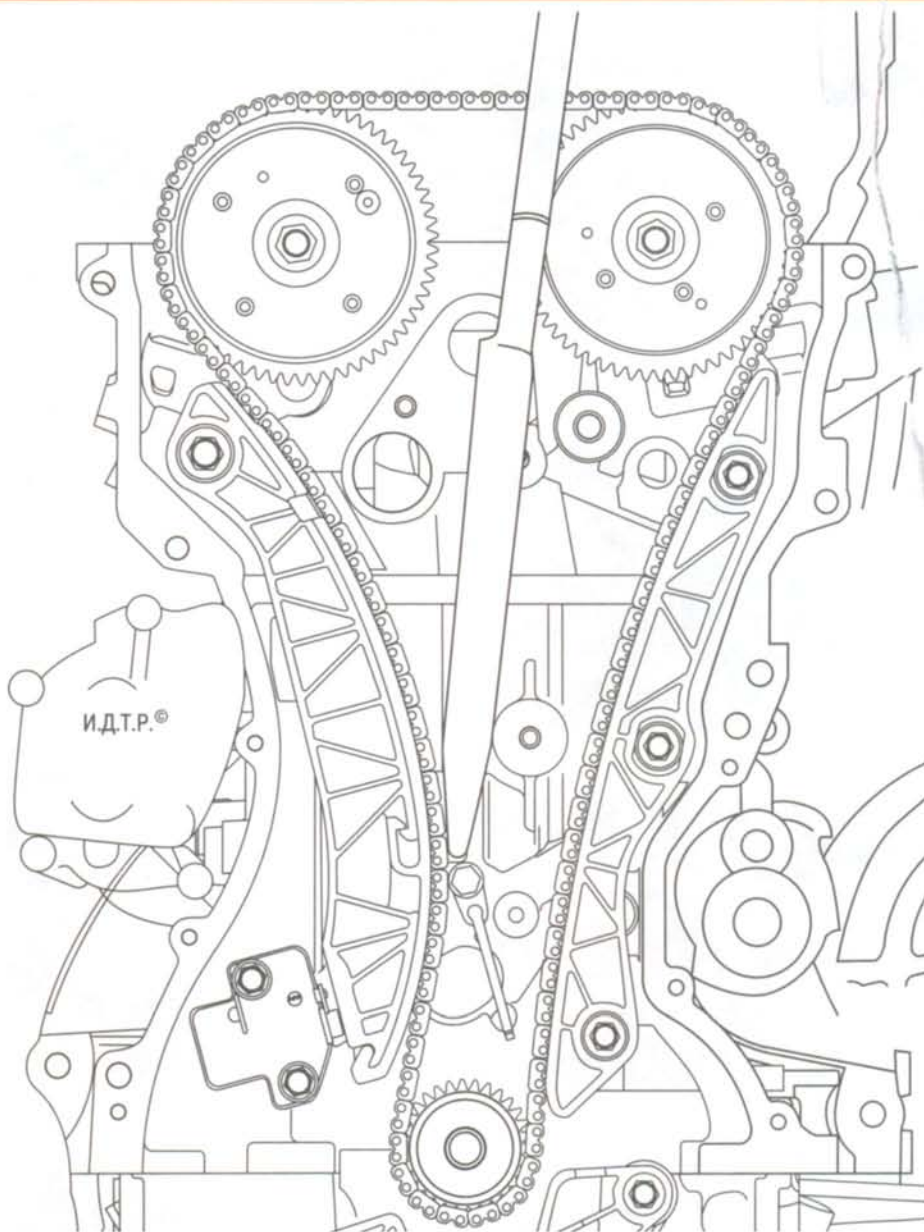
Отжатие башмака цепи привода газораспределительного механизма
